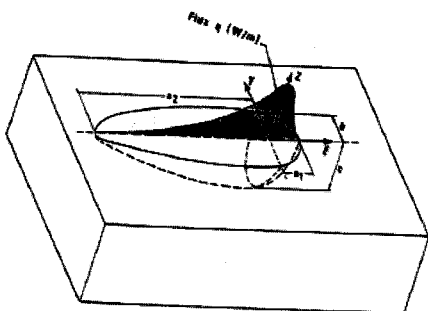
Goldak의 아크 용접 열원 모델⁶⁾
